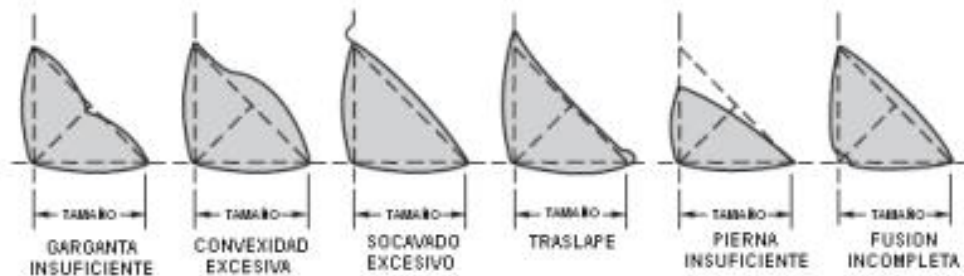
Aceptable o inaceptables perfiles de soldadura (de NMX-H-121-1988)
